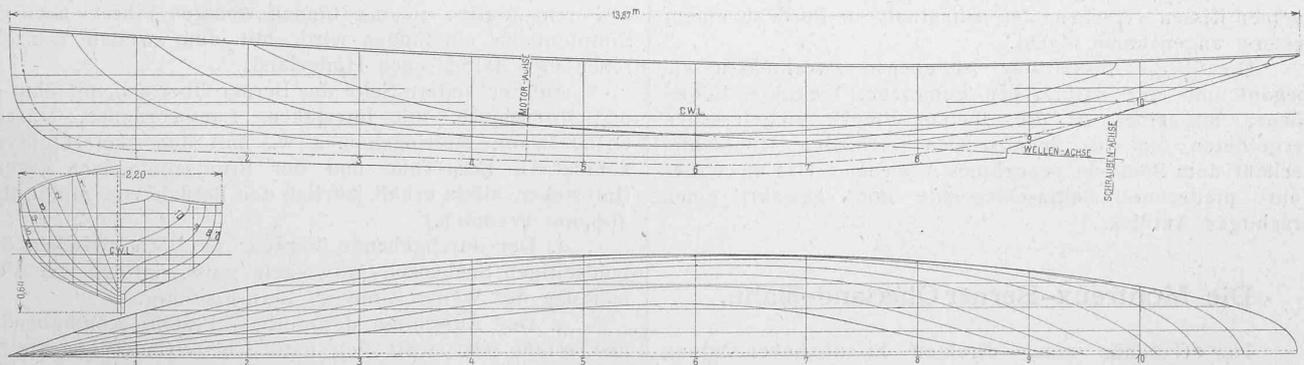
Motorboot «Fram». — Linienplan. Masstab 1:75.
